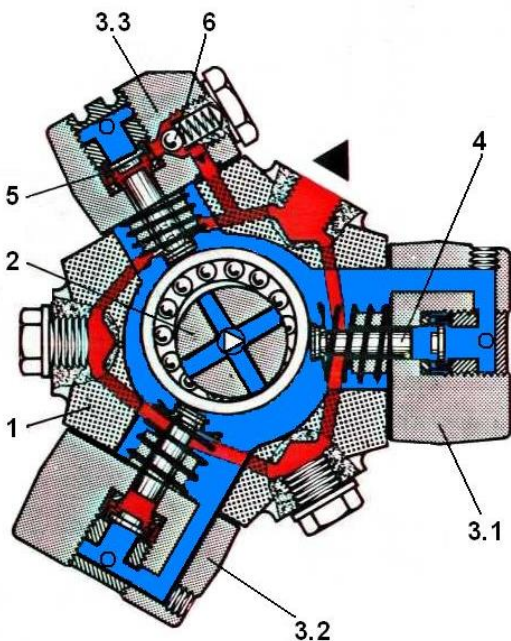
Радіально поршневий насос типу R2: 1 – корпус; 2 – ексцентриковий вал; 3 – елемент; 4 – поршень; 5 – всмоктувальний клапан; 6 – нагнітальний клапан
